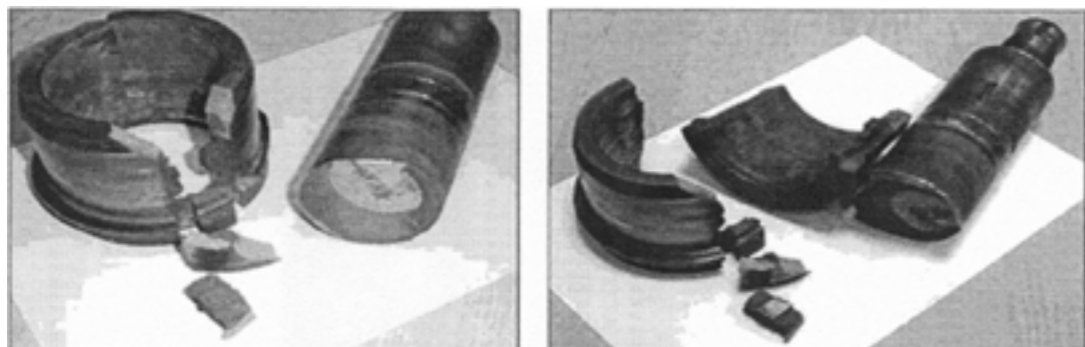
Корпус уплотнения и вал с усталостной трещиной
